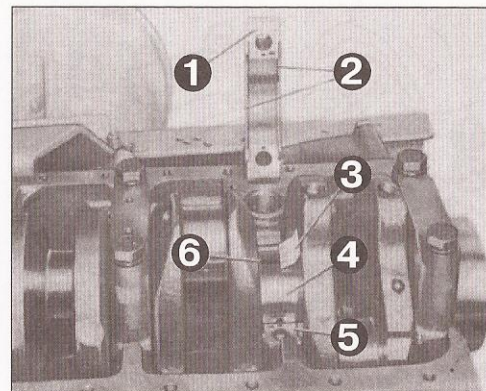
Проверка диаметрального зазора коренных шеек коленчатого вала методом «Plastigage».
